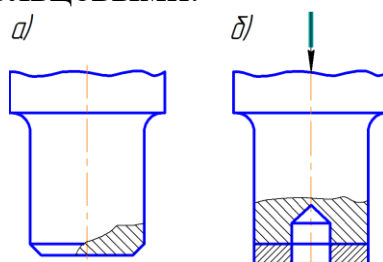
Опора вертикального вала – пяты: а – сплошная, б – кольцевая.
